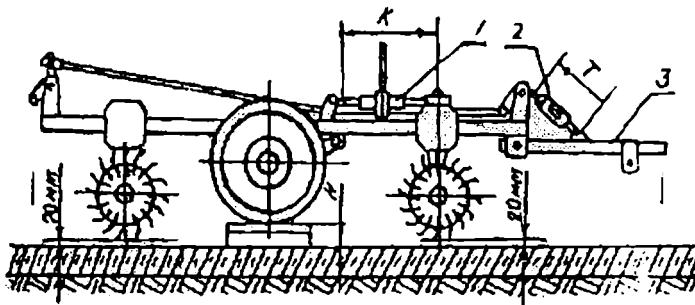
Схема бороны игольчатой БИГ-ЗА
